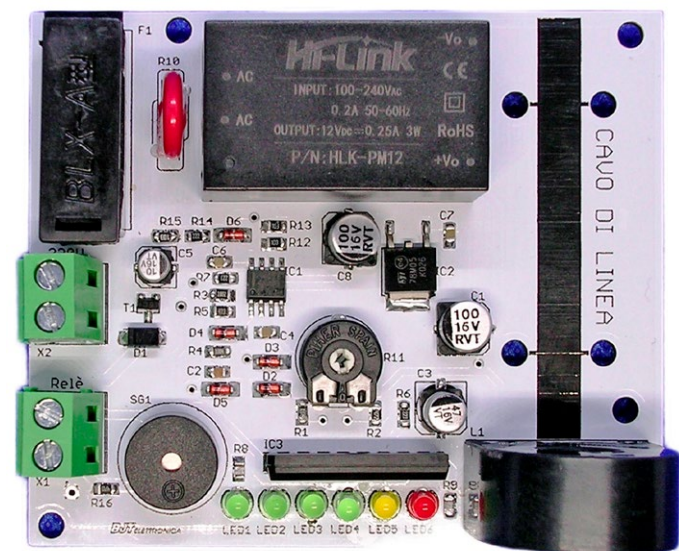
Circuit imprimé complet et assemblé pour mon prototype.
